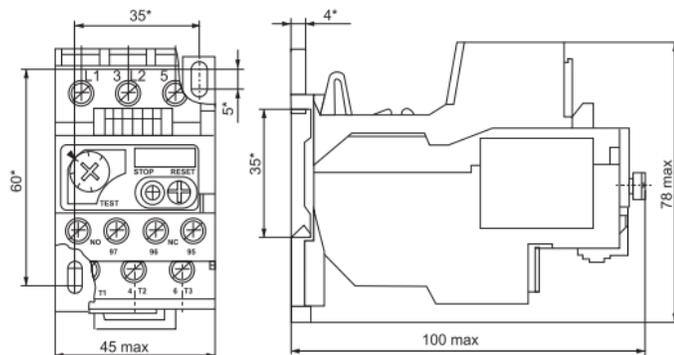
Реле типа РТЛ-3000, РТЛ-4000
